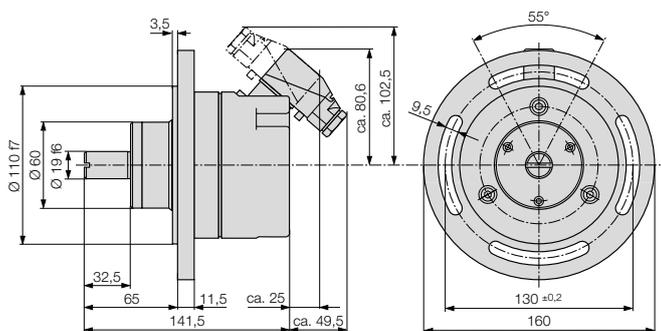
KINAX WT 707 mit Steckverbinder und Flansch.
